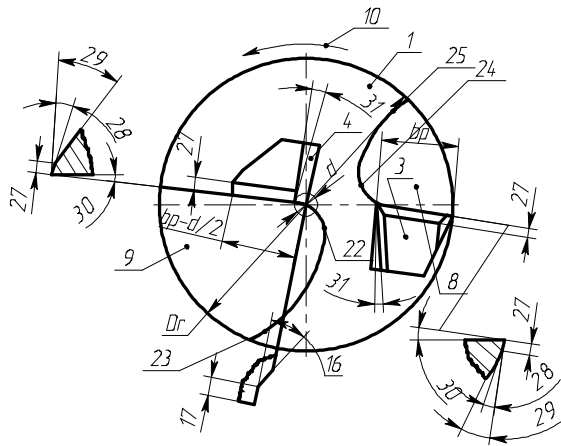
Вид на резцовую головку по стрелке К с исполнением 4 корпуса.
